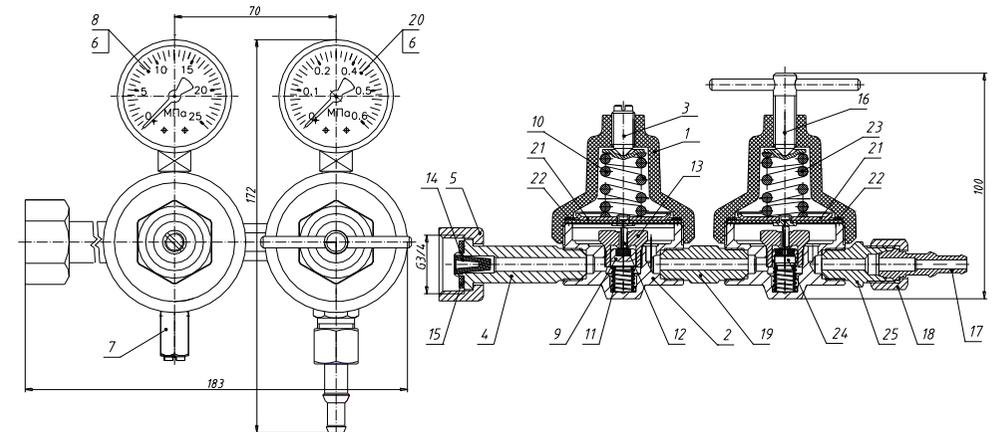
Редуктор баллонный газовый двухступенчатый:
